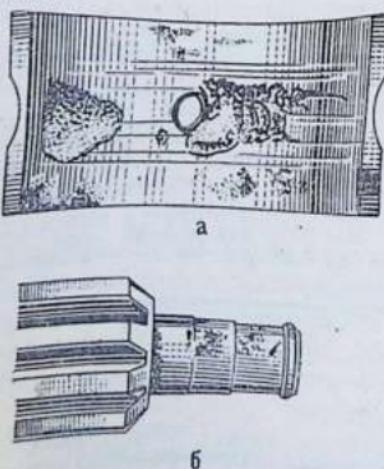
Внешний вид деталей, претерпевших изнашивание схватыванием:
